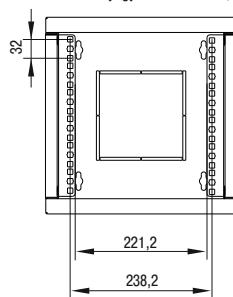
Габаритные и установочные размеры шкафа / Figure 1 – Overall and installation dimensions of the cabinet / 1 – suret – Škaftyň garabittik jäne ornatu ölçemder / Рисунок 1 – Габаритні та установчі розміри шафи
